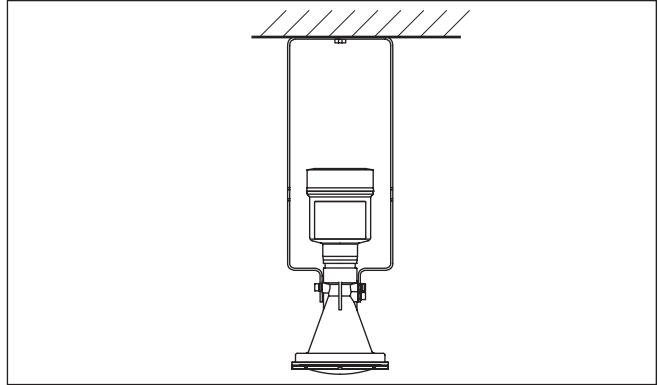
Montaggio sul cielo tramite la staffa di montaggio lunga 300 mm
